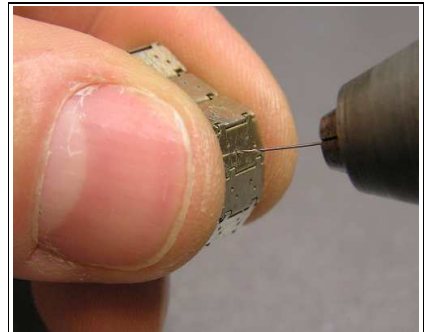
Der Menck 152 hat 26 Ketten-glieder je Kette. Der Menck 154 bekommt 29 Stück. Die Löcher mit 0,3mm Bohrer ausbohren.
